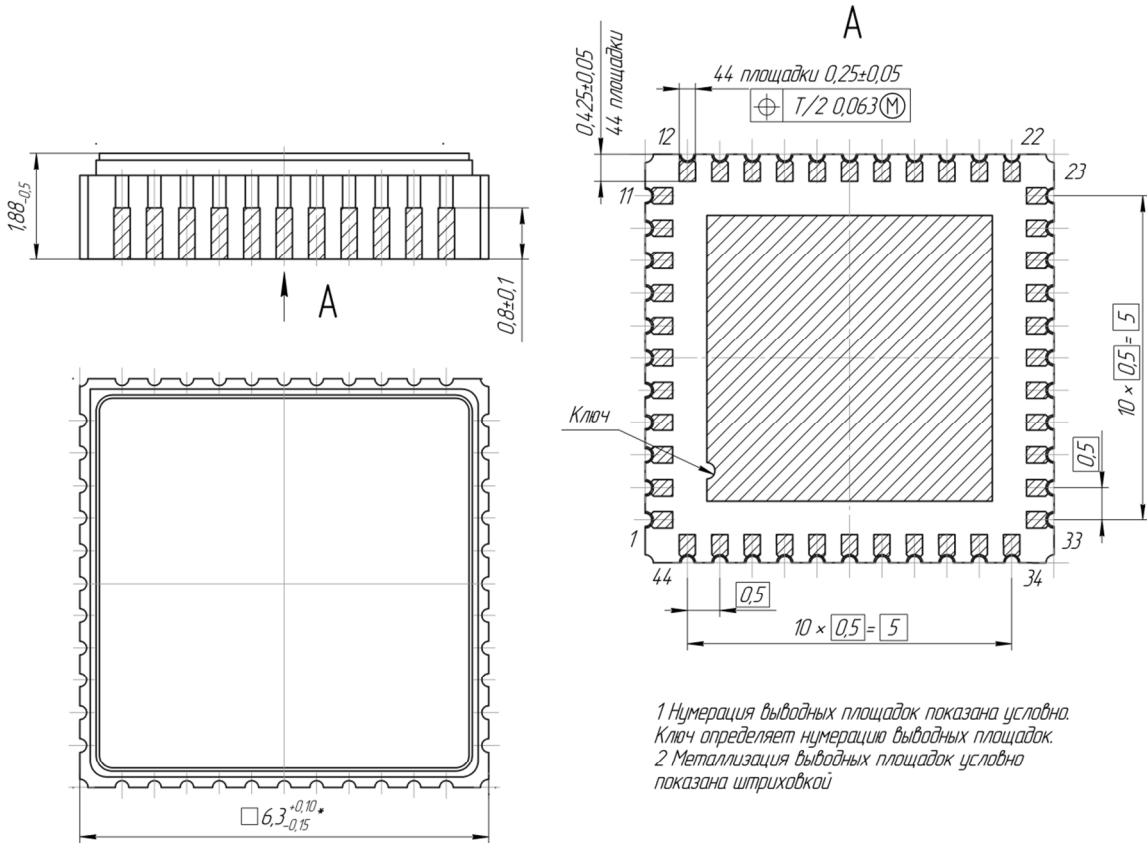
Габаритный чертёж корпуса МК 5165.44-1.
